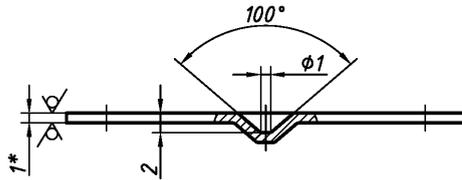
Оформление рабочего чертежа сборочной единицы «Лепесток реле», образованной пайкой
